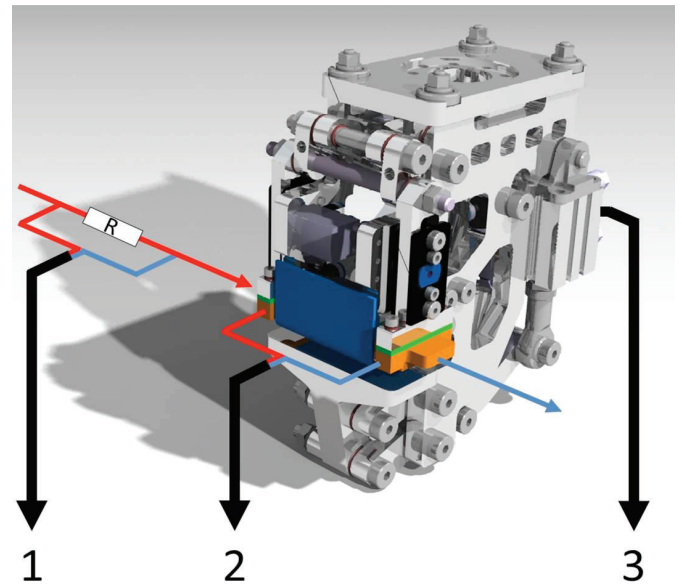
Endeffektor für das elektrische Widerstandsschweißen
